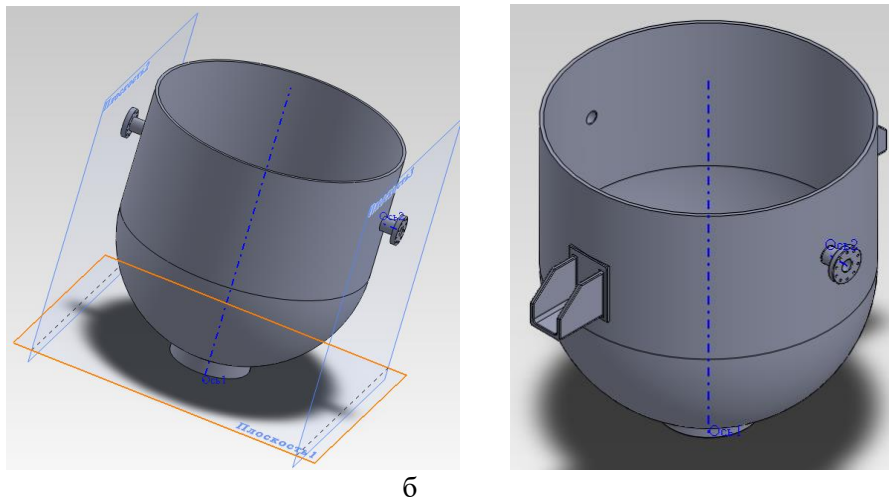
а) корпус реактора; б) фланцевое соединение на корпусе
